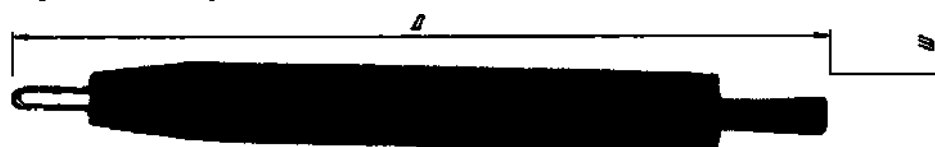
Внешний вид и размеры щётки для чистки слухового аппарата
